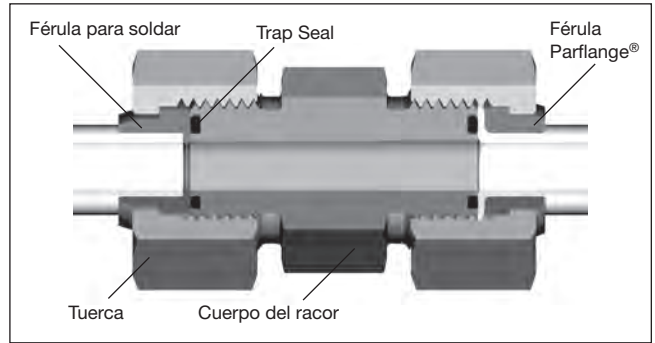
Vista seccionada de la unión O-Lok® con conjuntos soldados (LHS) y embridados
